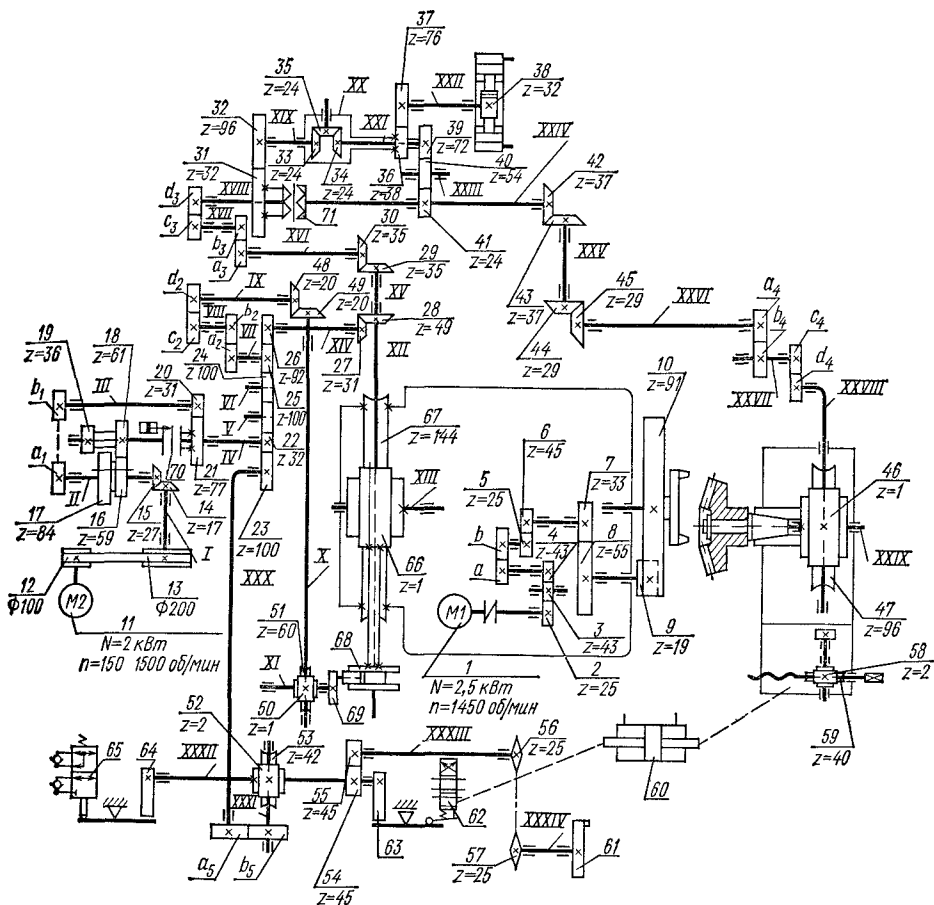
Кинематическая схема станка мод. 5С280П для нарезания конических колес с круговыми зубьями
